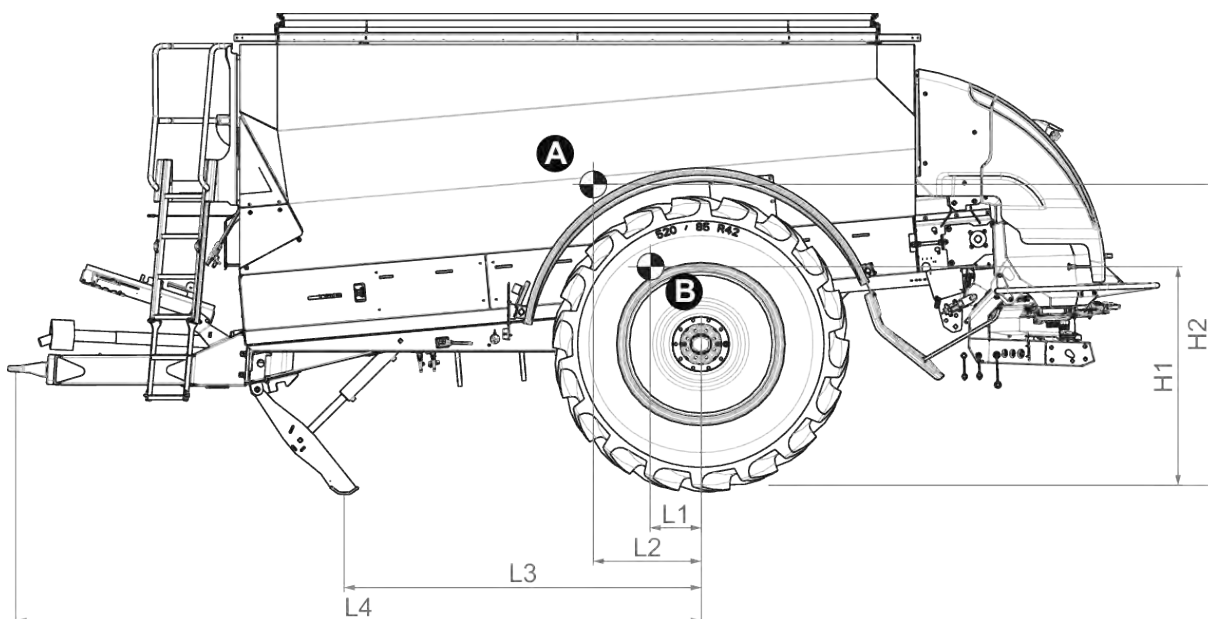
Schwerpunktlage in Untenanhängung, Achsposition vorne
